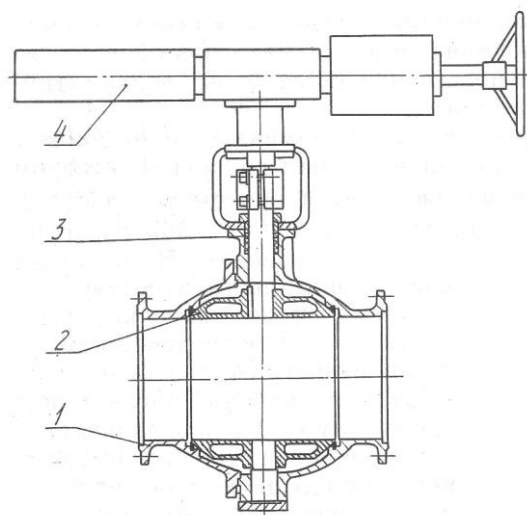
Отсечной шаровой клапан: 1 – корпус; 2 – шаровой затвор; 3 – уплотнительный узел; 4 – пневмопривод
